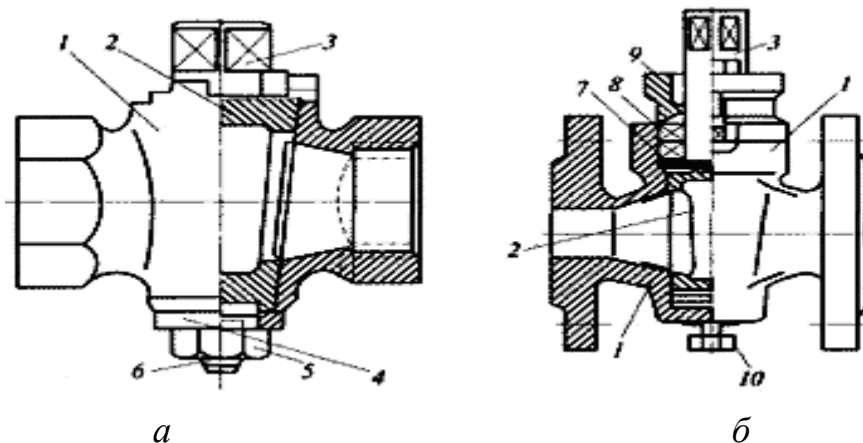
Крани: *а* – натяжний газовий муфтовий; *б* – сальниковий; 1 – корпус; 2 – пробка; 3 – чотиригранна головка; 4 – шайба; 5 – гайка; 6 – шпилька з різьбленням; 7 – опорне кільце; 8 – сальникове набивання; 9 – кришка сальника; 10 – болт
